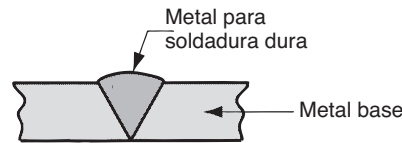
Soldadura dura. La unión consiste en metal (de relleno) para soldadura dura; no se funde el metal base en la unión.
